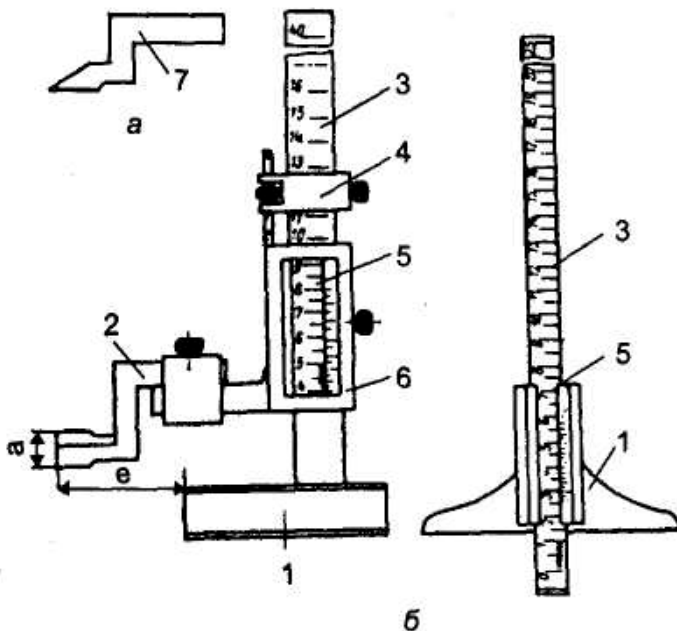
Штангенрейсмас (а) и штангенглубиномер б):
